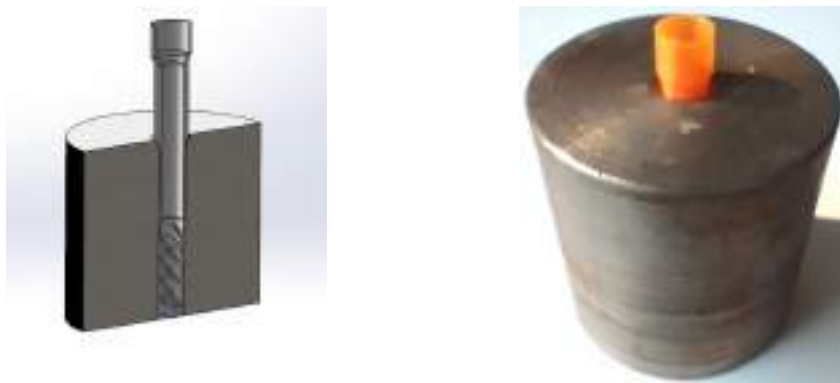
Пресс-форма для изготовления фрезы, заключенная в стальную оболочку
